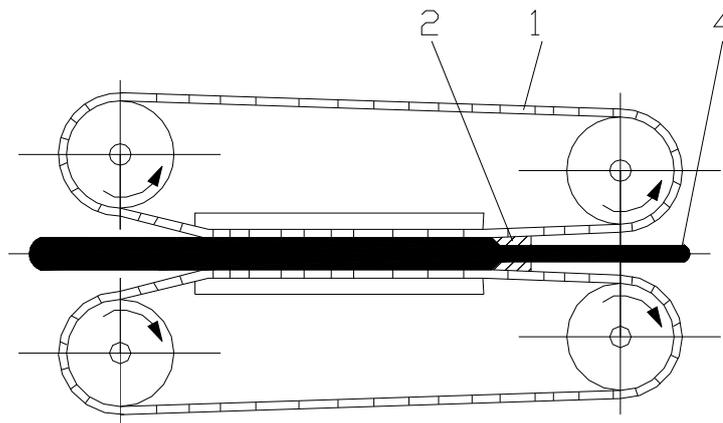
Схема процесса непрерывного прессования способом Лайнекс:
